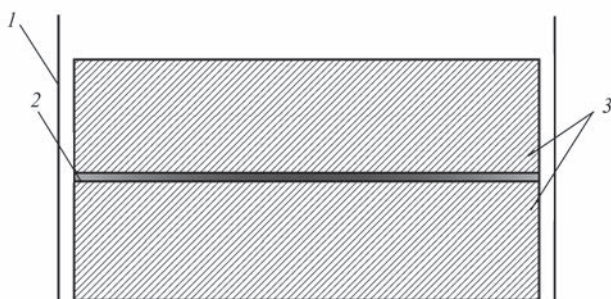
Схема поперечного перерізу шихтової заготовки: 1 — невитратний короб; 2 — шар порошку TiO_2 ; 3 — шихтова заготовка
